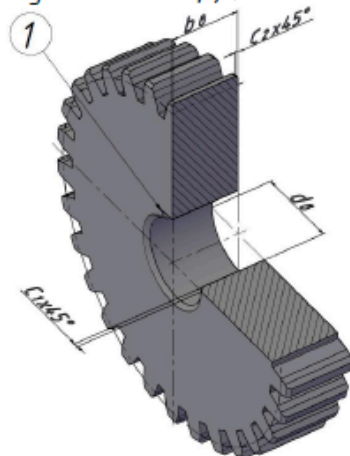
Циліндричне зубчасте колесо: 1-паз під призматичну шпонку.
